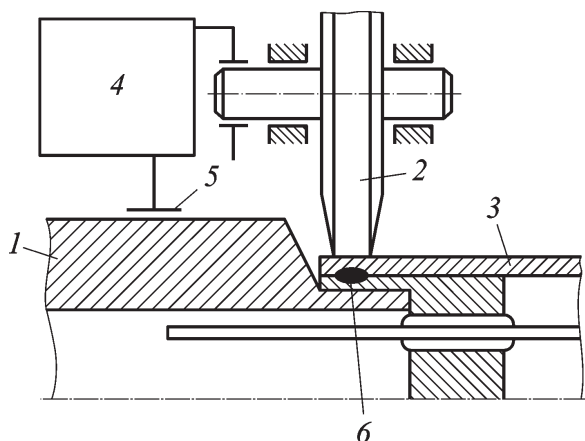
Схема сварки при двустороннем подводе сварочного тока
